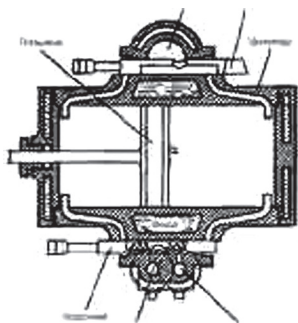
Схема газопоршневого двигателя Филиппа Лебона
